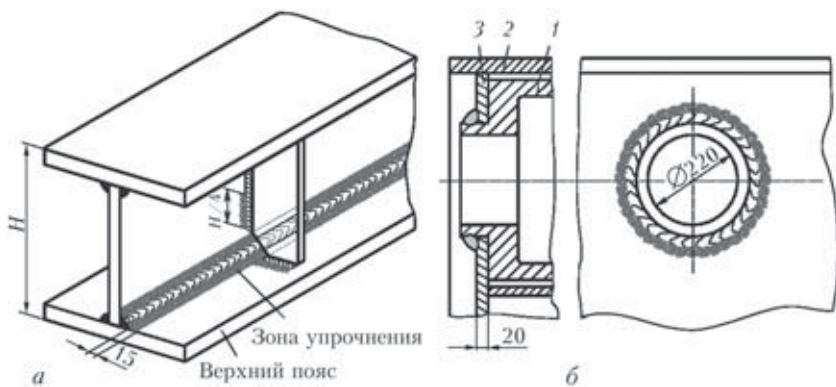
Зоны упрочнения сварных соединений (затемнены) подкрановых балок (а) и балансира колодцевых кранов (б): 1 — втулка; 2 — верхний пояс; 3 — стенка
